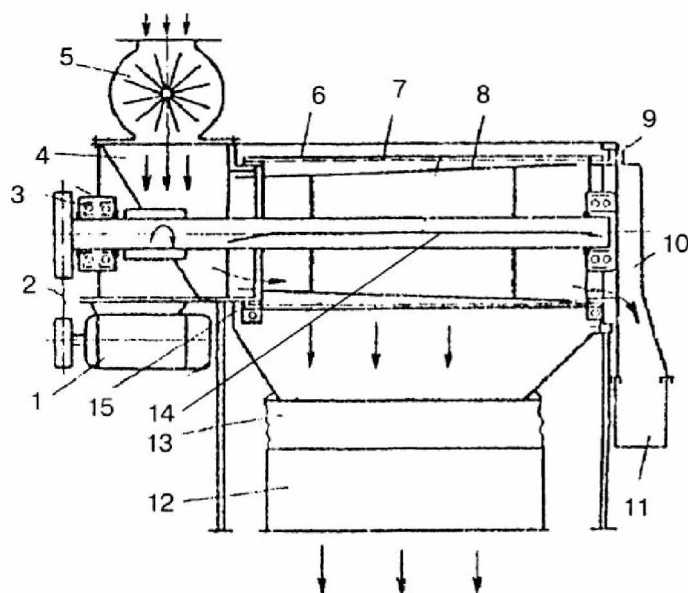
Просіювач Ш2-ХМВ: 1 – двигун; 2 – клинопасова передача; 3 – підшипниковий вузол; 4 – корпус; 5 – шлюзовий завантажувальний патрубок; 6 – каркас сита; 7 – ситовий барабан; 8 – гонки; 9 – кришка ситового барабану; 10 – кришка збірника відходів; 11 – збірник відходів; 12 – магнітні уловлювачі; 13 – гнучкий патрубок; 14 – вал; 15 – кільце для сита
